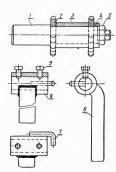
Устройство для одновременного фрезерования двух пазов на пальце рессоры автомобиля ГАЗ-51:
